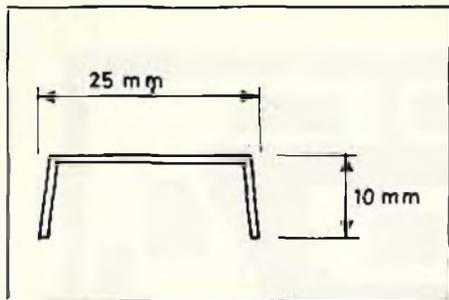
Forma e dimensioni (in mm.) della L2.
